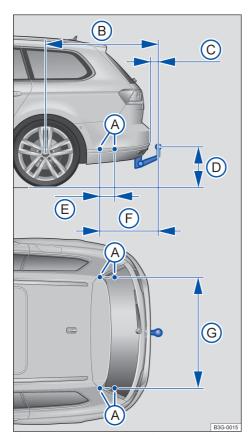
Dimensões e pontos de fixação para instalação posterior de um dispositivo de reboque (Passat Variant).
